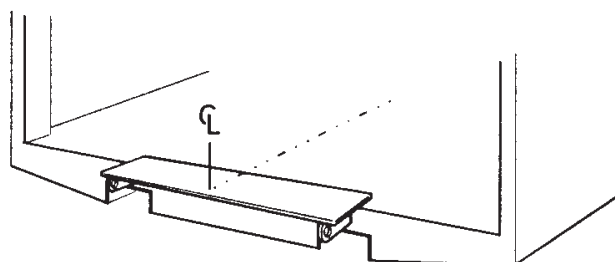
Atornillar o soldar por puntos el accesorio de montaje en la barra trasera N.º de ref. 72650TL para ZHD 3000
